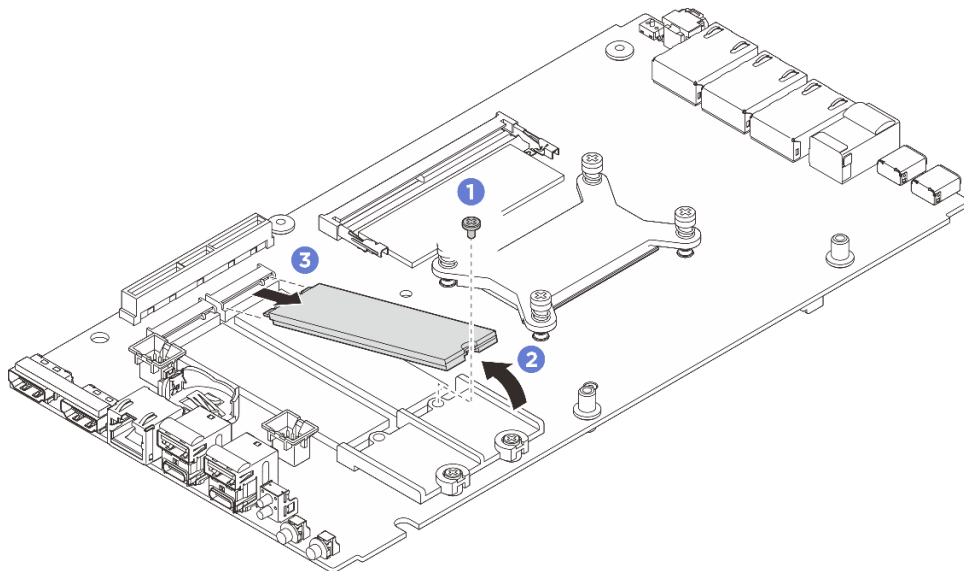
Entfernen des M.2-Laufwerks (Formfaktor 2280)
